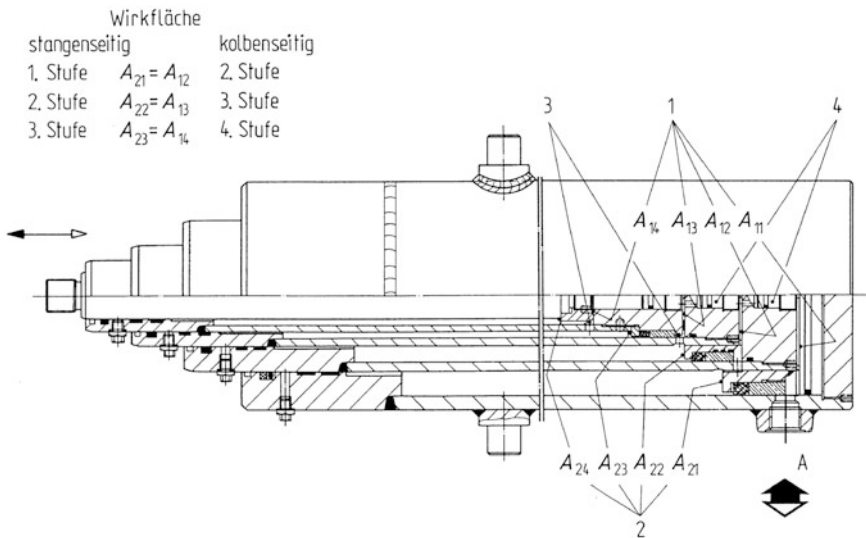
Gleichlauf-Teleskopzylinder, 4stufig, Zylinder mit Drehzapfenbefestigung, Zylinderkopf geschweißt (ZYG, Toussaint & Hess). 1 kolbenseitige Verdrängerräume, 2 stangenseitige Verdrängerräume, 3 seitliche Bohrungen, 4 Rückschlagventile; Kolbendichtungen aus Mehrfach-Lippensatz (Dachmanschetten-Dichtsatz) mit Führungsbändern und Lagermetall-Führungsbuchse; Stangendichtungen aus O-Ring mit Stützring und Führungsbändern
